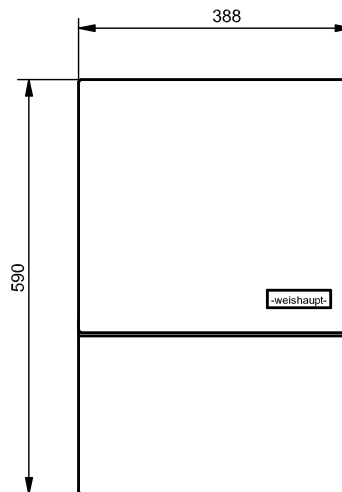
Dimensioner för väggmonterad kaskadreglering
